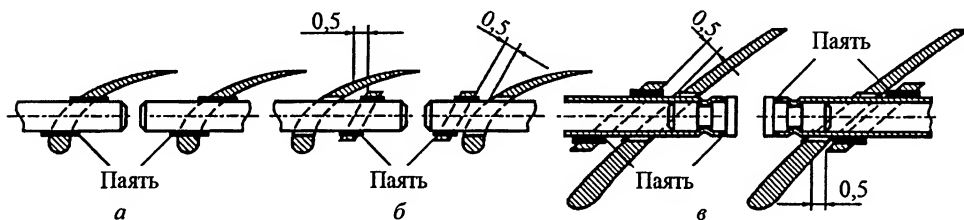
Конструкция проволочных и трубчатых бандажей: проволочный, припаянный (а) и неприпаянный (б) к лопатке; трубчатый (в)
